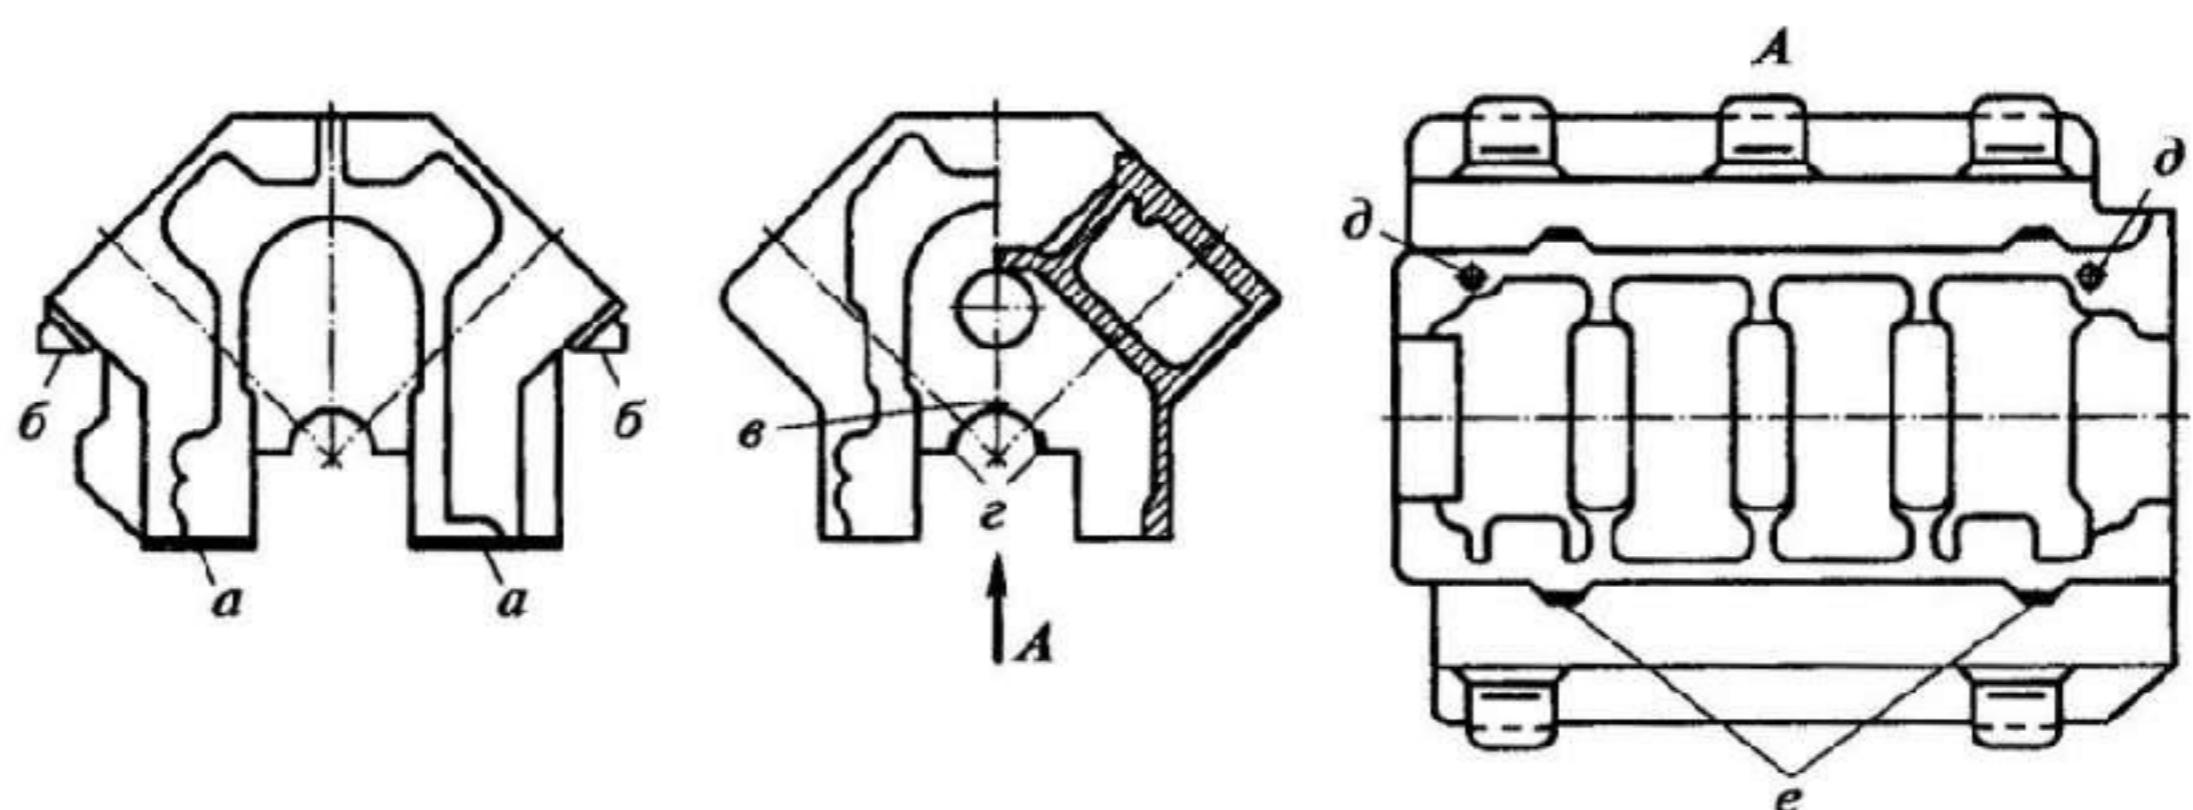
Расположение установочных поверхностей (а—е) на заготовке V-образного блока цилиндров
